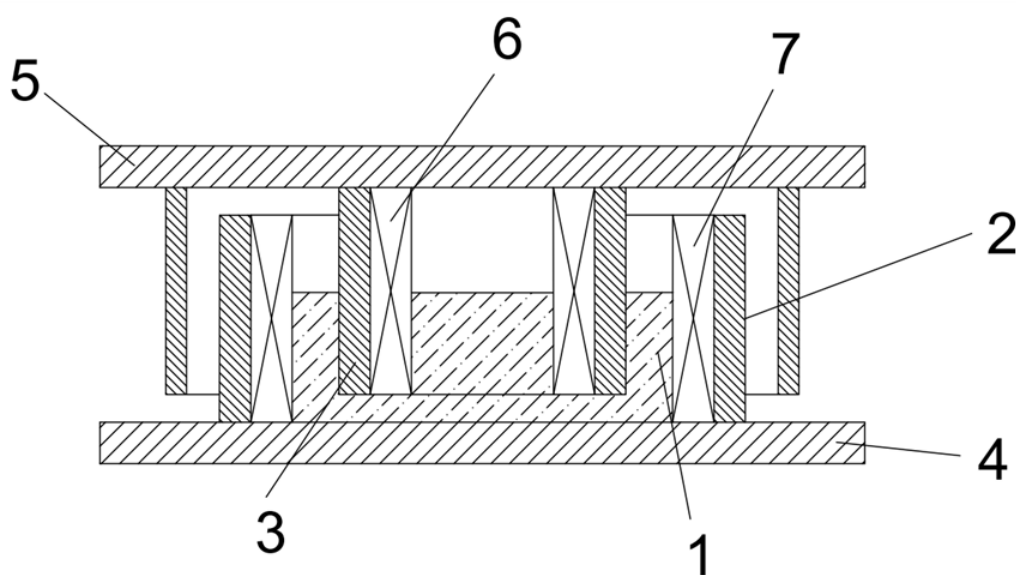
Феррожидкостное устройство активной вибрационной защиты: 1 – объем ферромагнитной жидкости, 2 – цилиндрический корпус, 3 – поршень, 4 – нижняя присоединительная плита, 5 – верхняя присоединительная плита, 6 – вихревая герметизированная катушка индуктивности, 7 – герметизированная кольцевая катушка индуктивности
